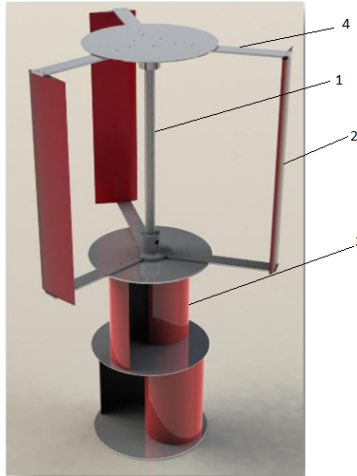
Приклад конструктивної схеми комбінованого ротора з вертикальною віссю обертання: 1 – вал; 2 – ротор Дар'є з трьома прямими лопатями; 3 – стартер (двоступінчатий ротор Савоніуса з двома лопатями, рознесеними по фазі); 4 – траверси
